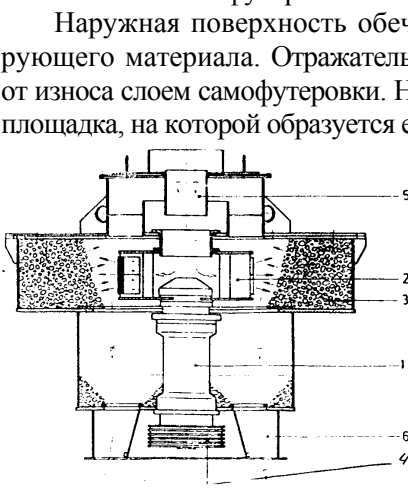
Дробилка серии V – SBM: 1 – вал; 2 – ротор; 3 – автогенная самофутеровка; 4 – клиноременная передача; 5 – питающая труба; 6 – разгрузочный бункер
